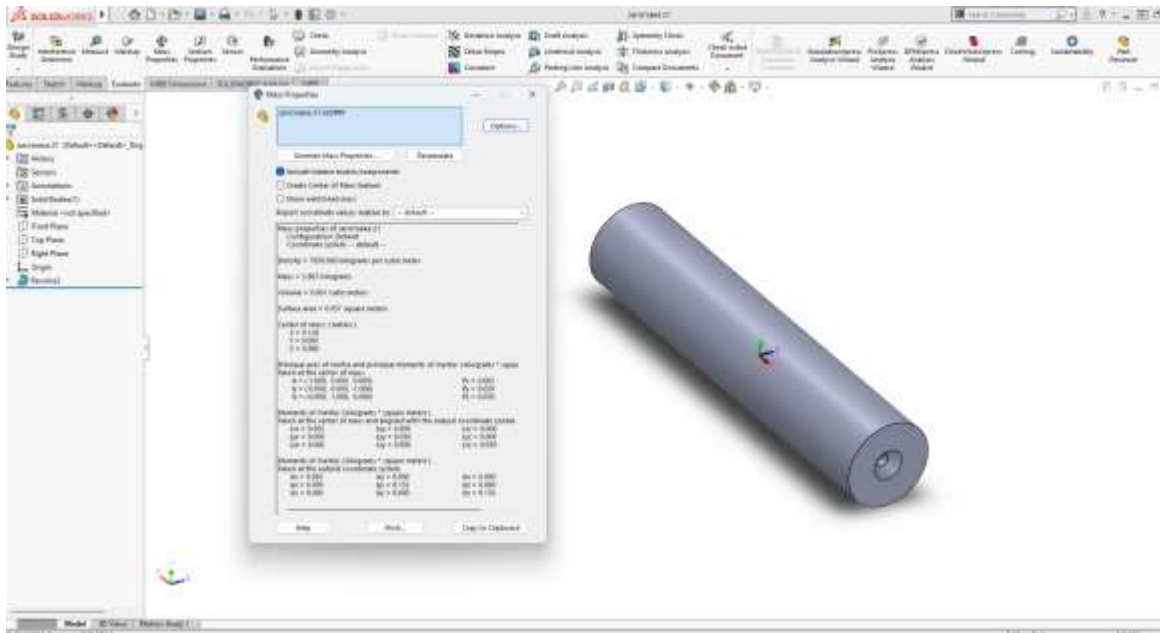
Обрахунки маси заготовки в програмі SolidWorks
